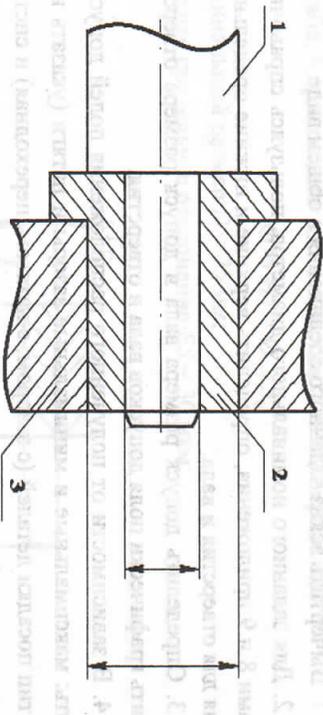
Схема соединения: 1 – вал; 2 – вкладыш подшипника; 3 – корпус
